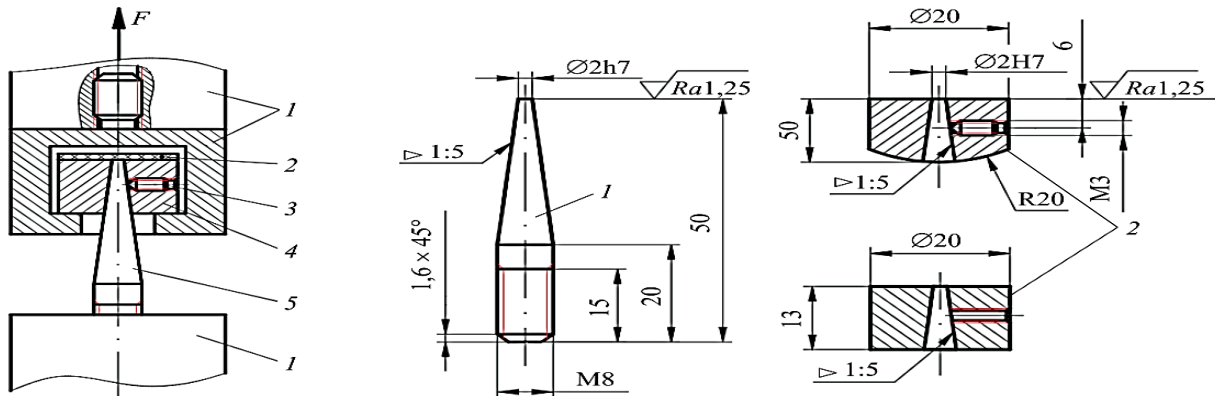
Конструктивные схемы экспериментальных ОС для оценки прочности сцепления ГПП толщиной $h_{п} \geq 0,3$ мм по штифтовому методу: 1 - оснастка для закрепления в разрывной машине; 2 - испытываемое покрытие; 3 - стопорный винт; 4 - конусная шайба (оправка); 5 - конический штифт.
